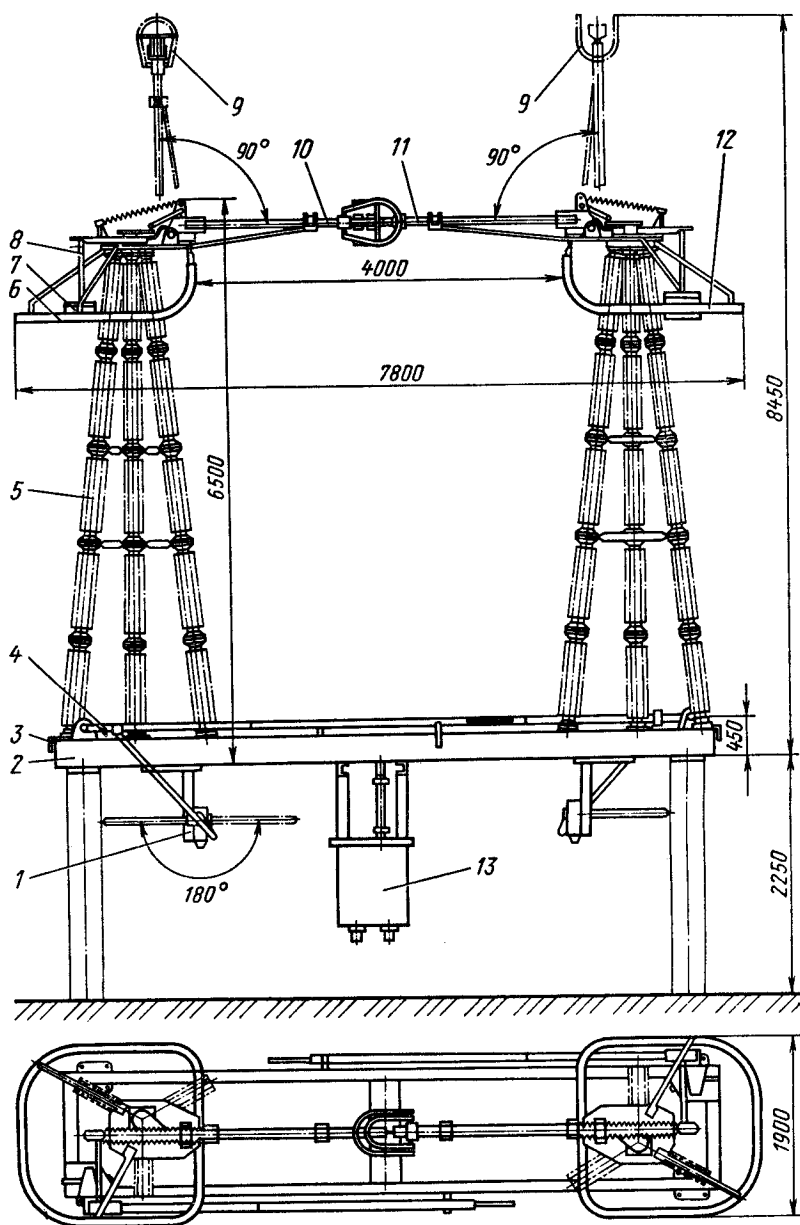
Разъединитель для наружной установки вертикально-поворотного типа РНВ-500:
